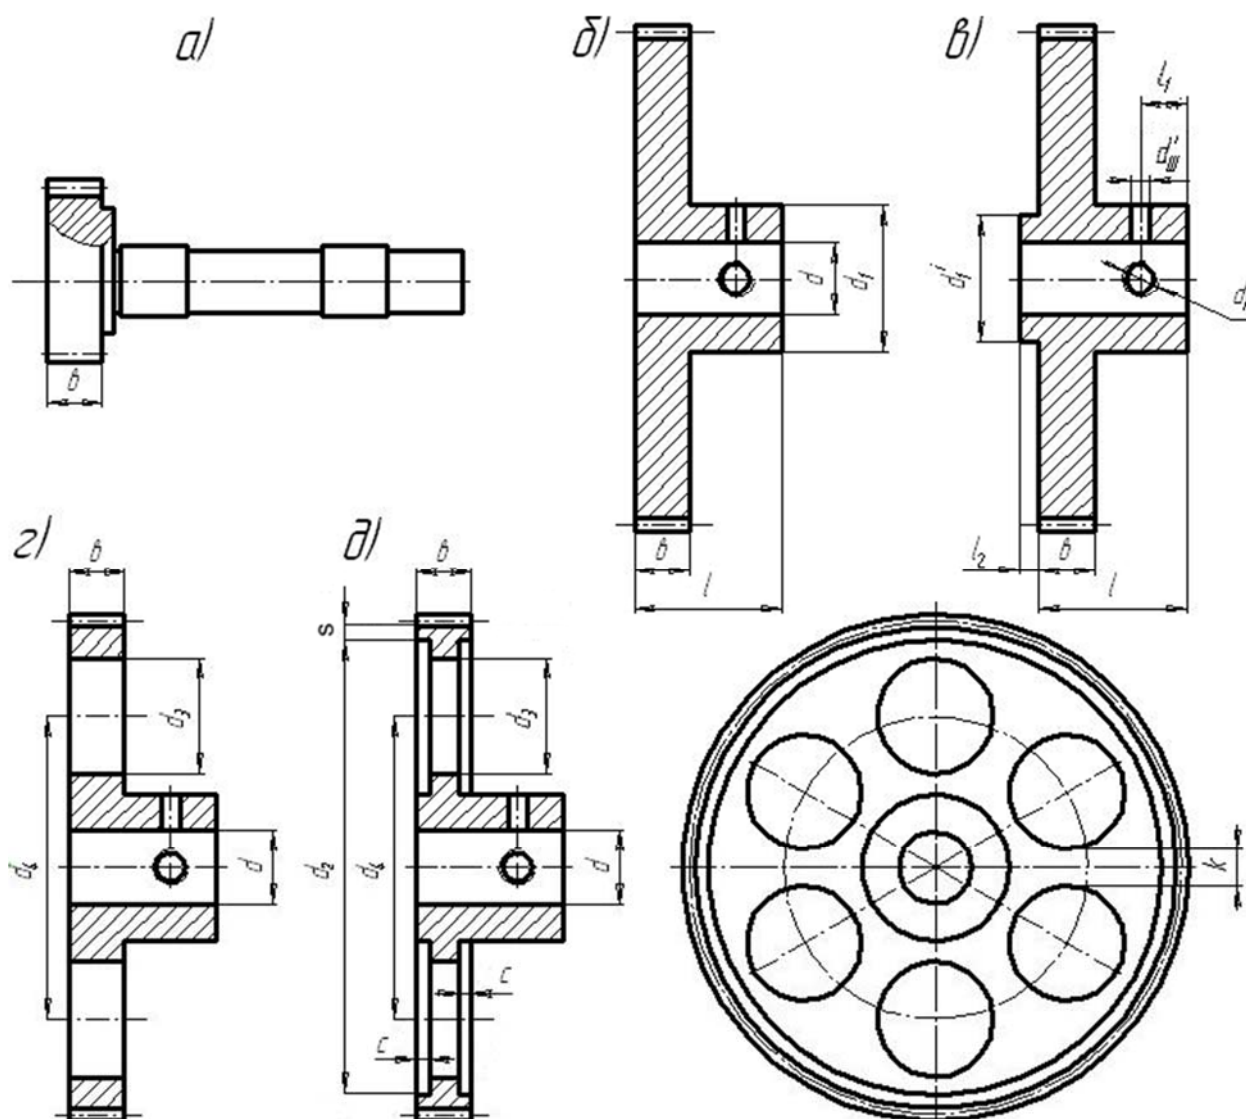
Типовые конструкции цилиндрических зубчатых колёс
